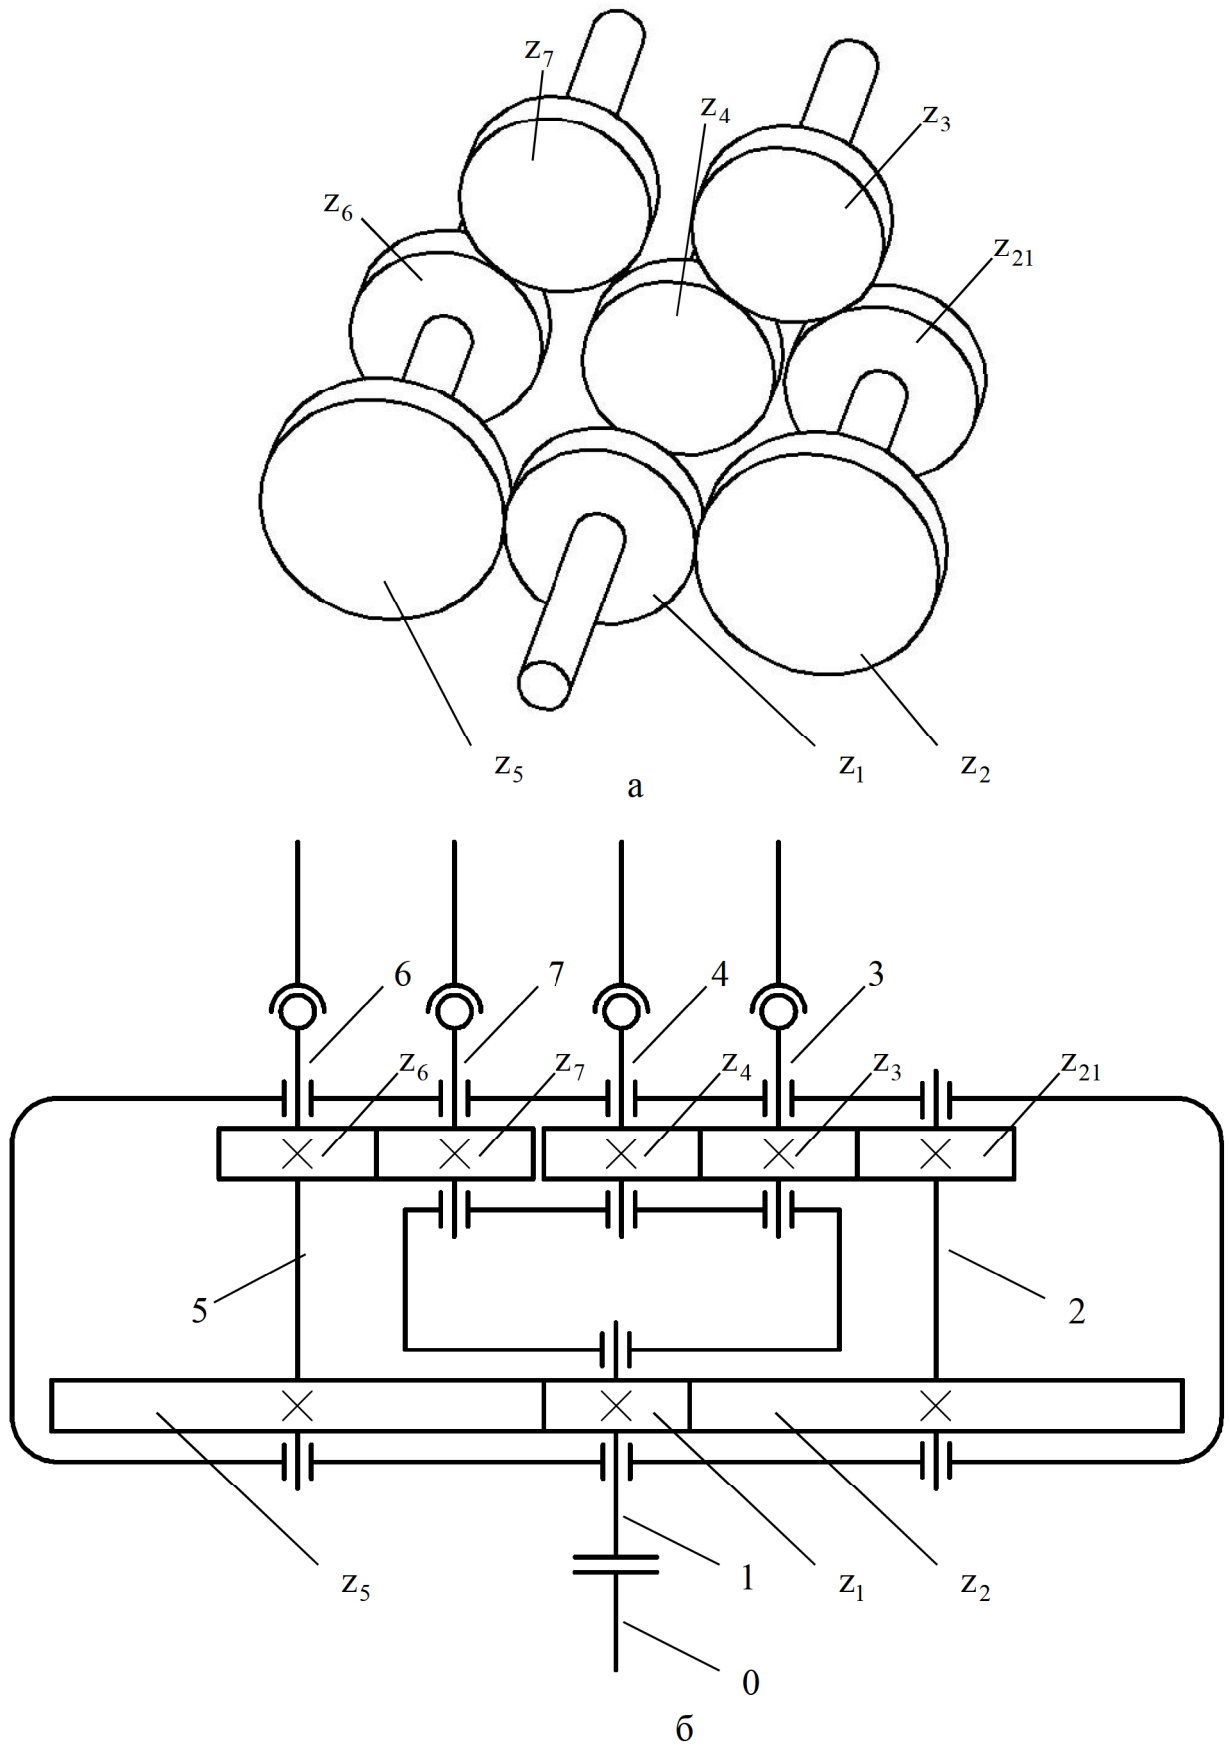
Кінематична просторова (а) і розрахункова (б) схеми редуктора
